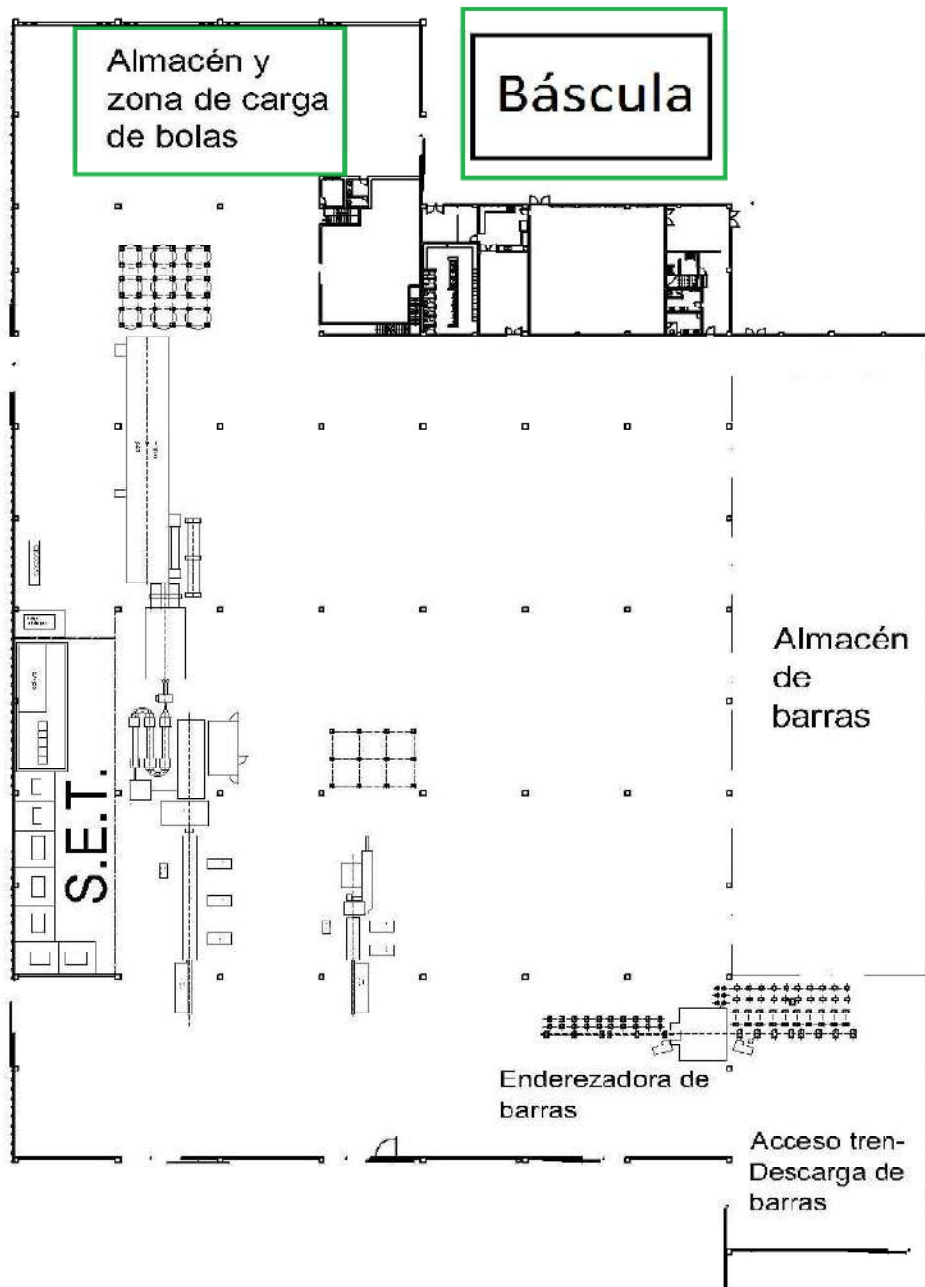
Lay-out de la planta. Se resalta sector de almacén de bolas.
